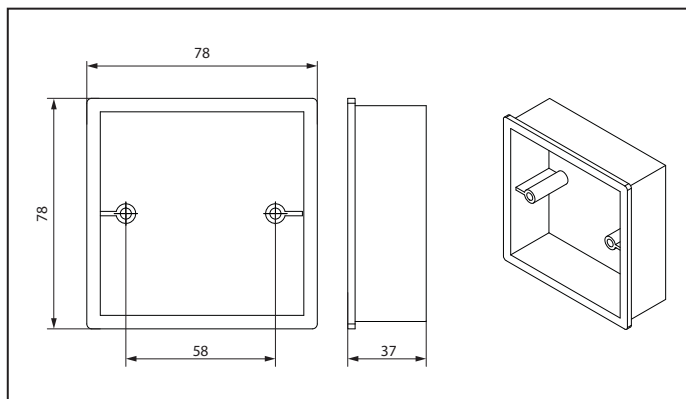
Габаритные размеры внутристенной монтажной коробки
